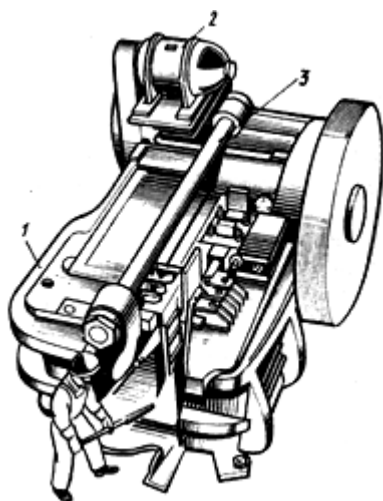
Общий вид ГКМ с вертикальным разъёмом штампов.
